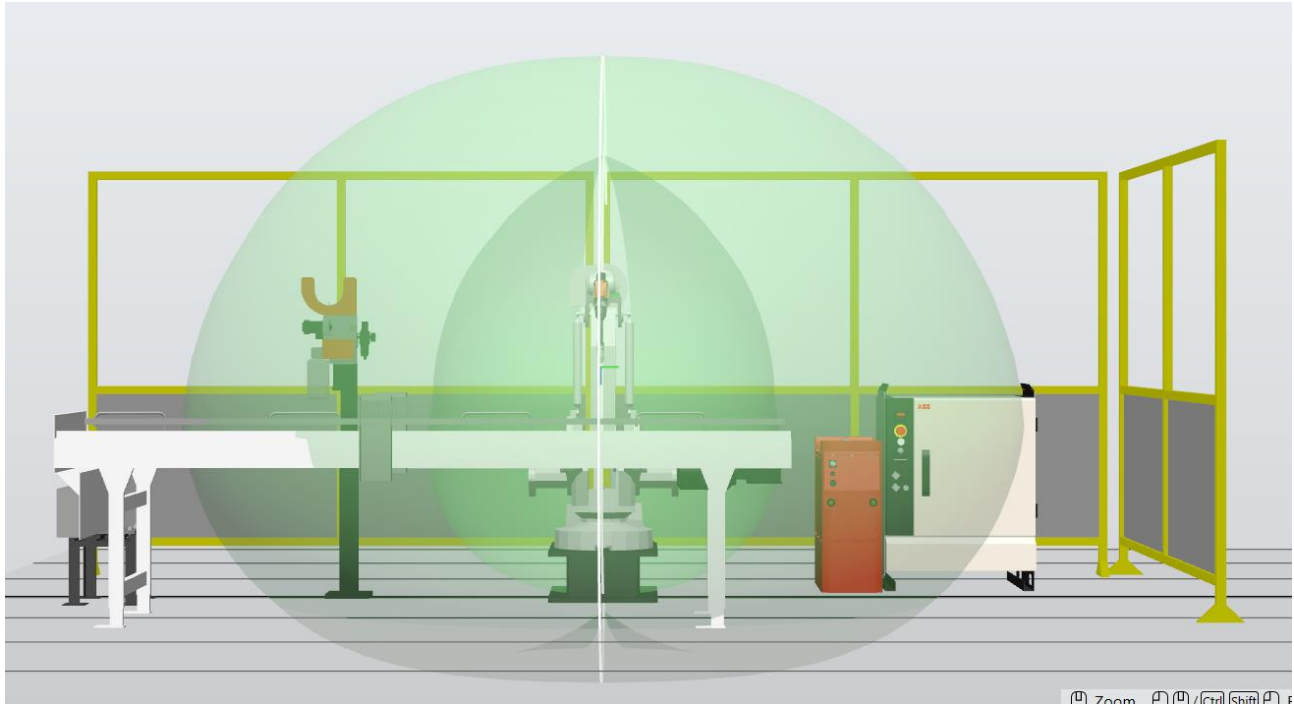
Робоча зона робота ABB IRB 1410-4/1.45 вертикальний зовнішній контур обмежується точкою TCP інструмента – зварювального пальника
